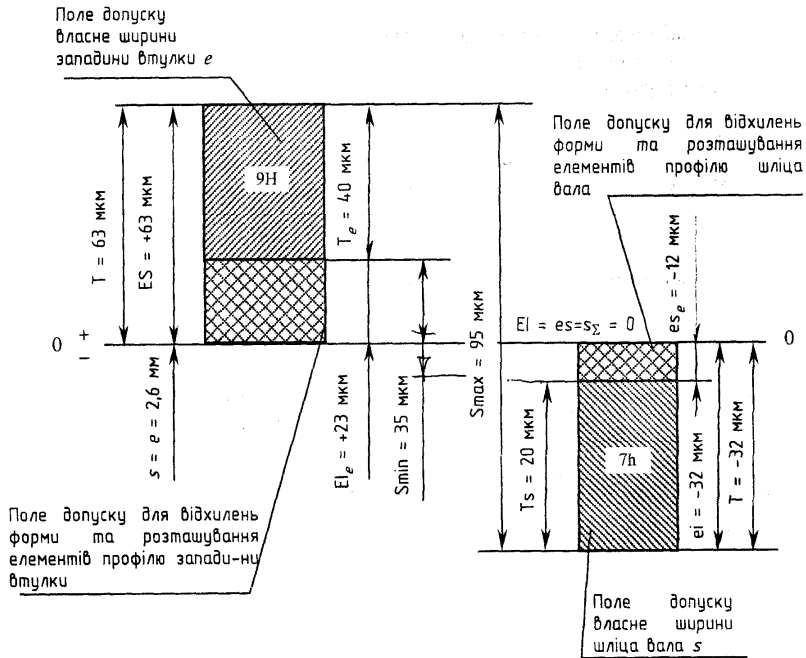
Схема розташування полів допусків евольвентного шліцевого з'єднання за центруючими бічними поверхнями шліців
